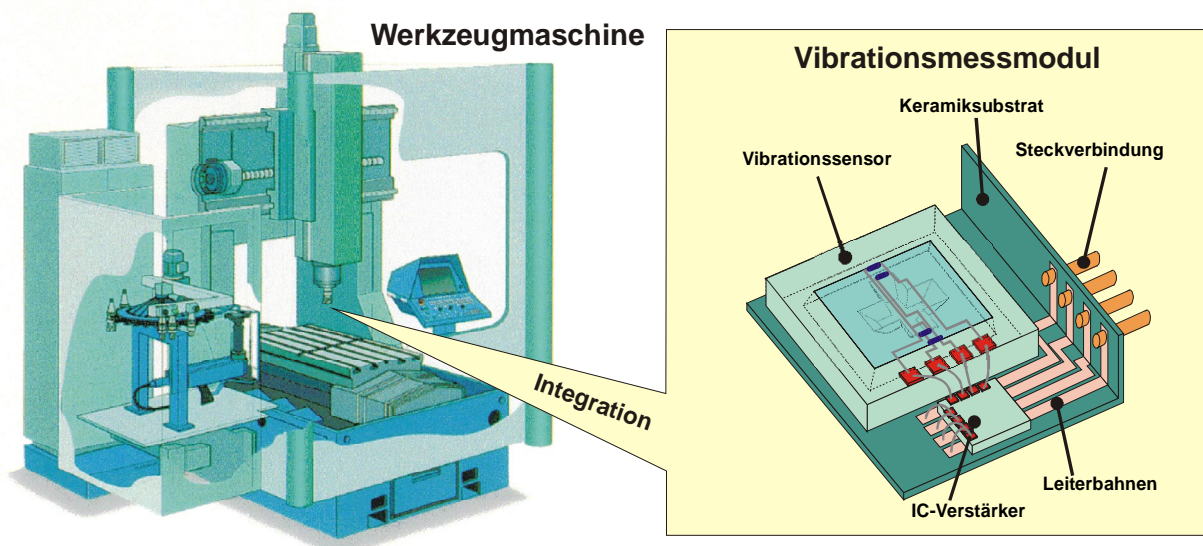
Konzeption einer Sensorintegration in Werkzeugmaschinen
